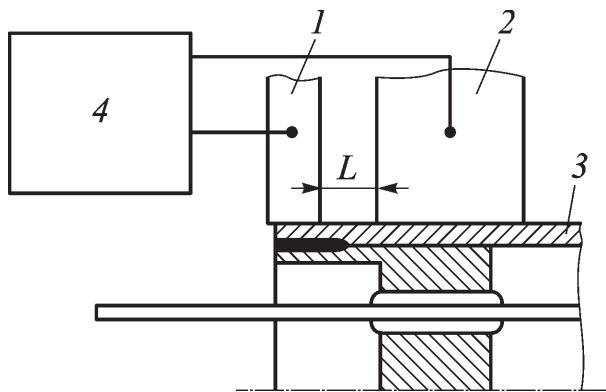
Схема сварки при одностороннем подводе сварочного тока
